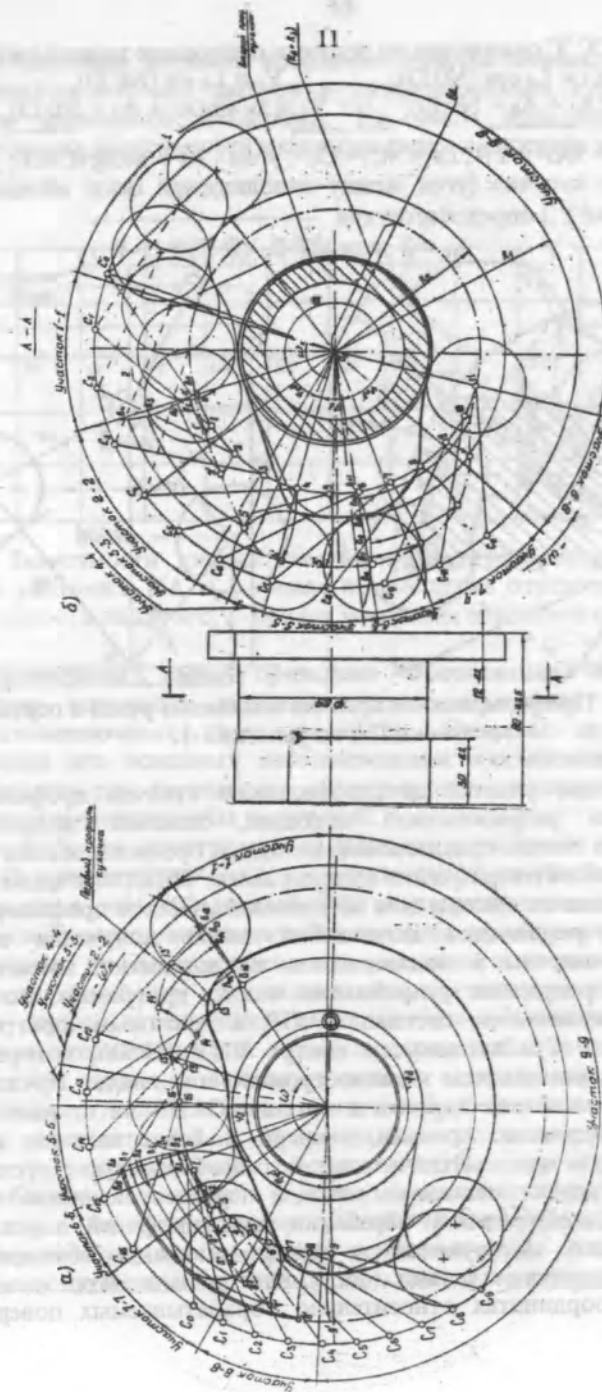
Кинематическая схема двухпрофильного кулачкового механизма
